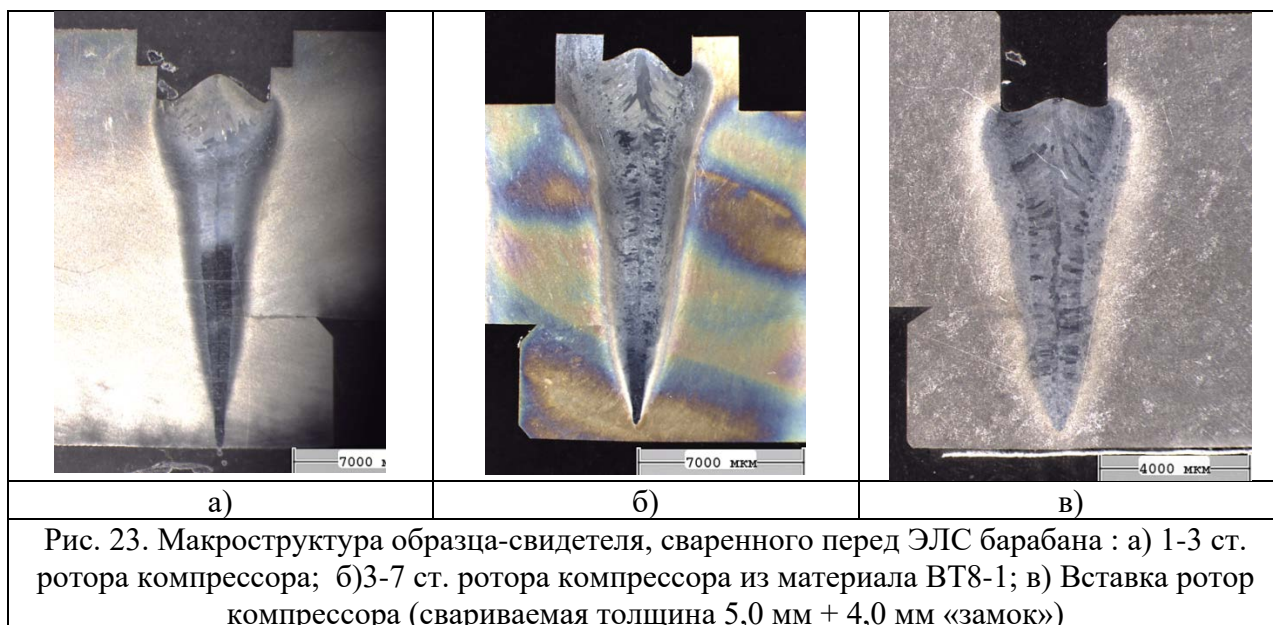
Макроструктура образца-свидетеля, сваренного перед ЭЛС барабана : а) 1-3 ст. ротора компрессора; б) 3-7 ст. ротора компрессора из материала ВТ8-1; в) Вставка ротор компрессора (свариваемая толщина 5,0 мм + 4,0 мм «замок»)
